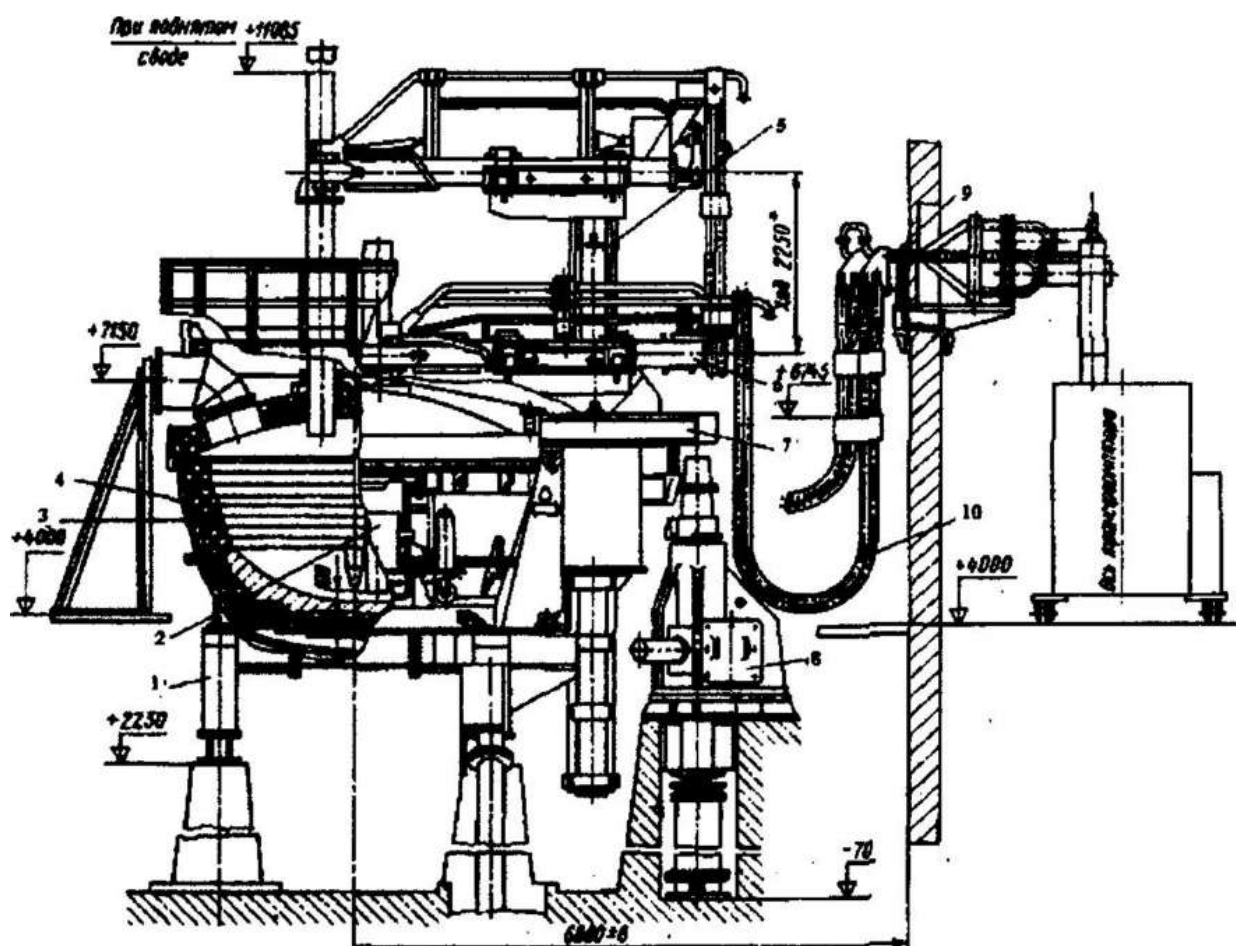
Конструкция дуговой печи ДСП – 100
